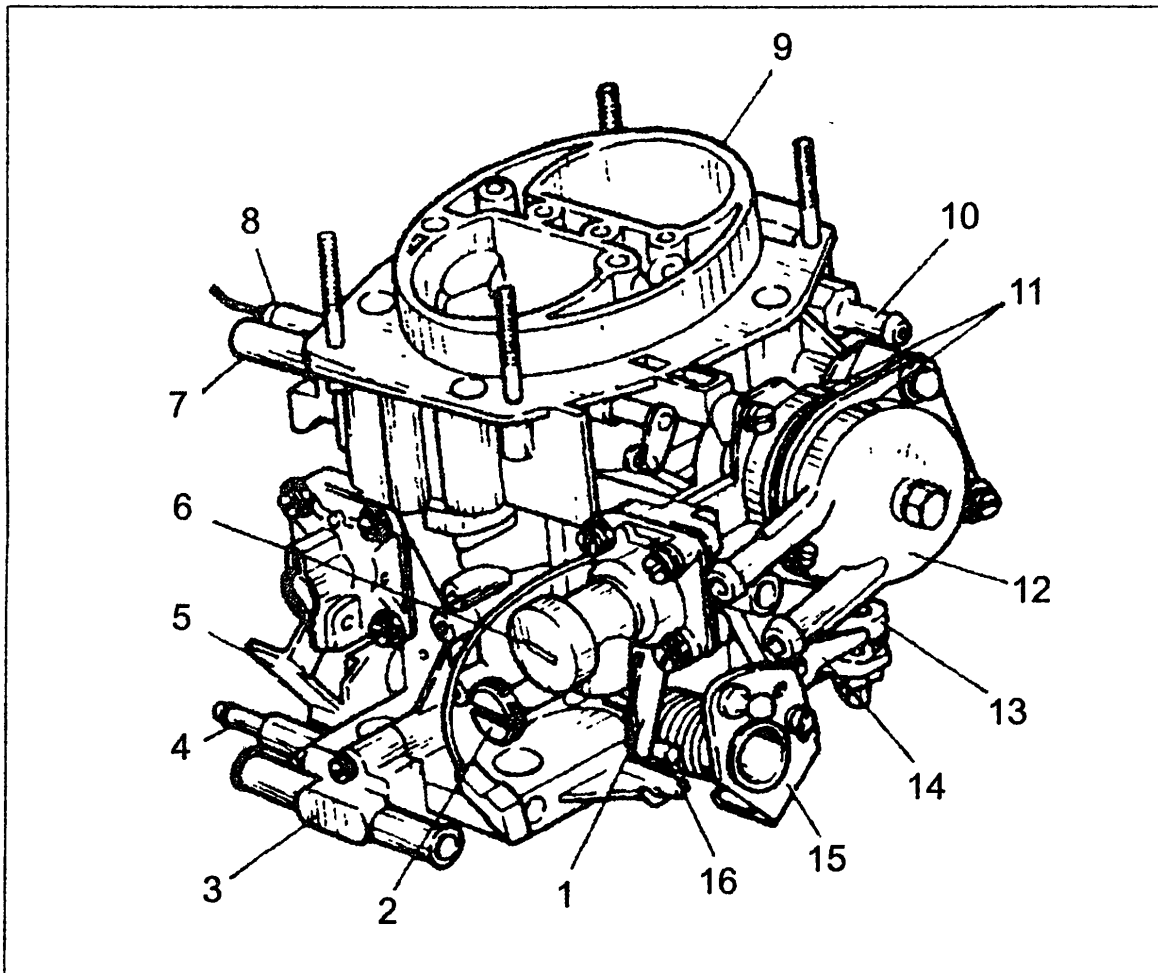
Внешний вид карбюратора ВАЗ-21083-1107010-62:
